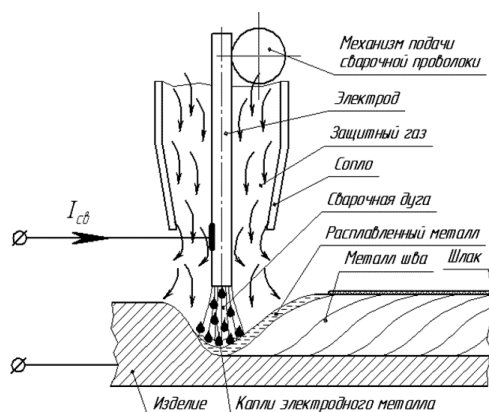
Эскиз механизированной сварки в среде смеси защитных газов
